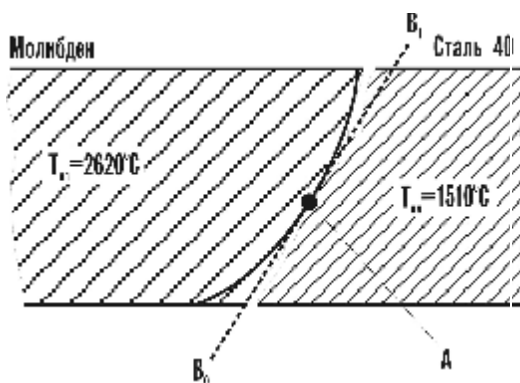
Геометрия стыкового соединения при сварке разнородных металлов
